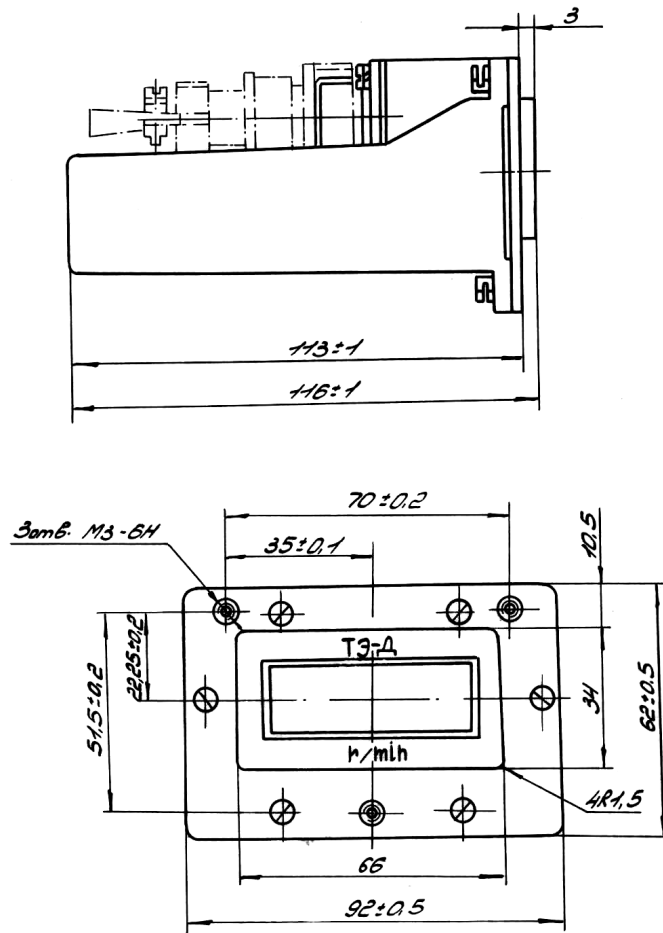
Габаритные размеры прибора показывающего ТЭ-Д
